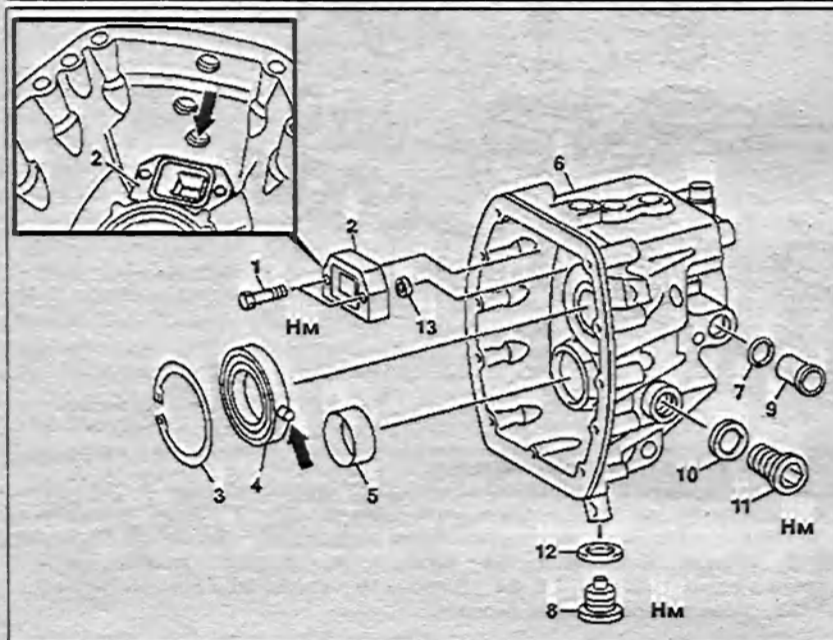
б. Задняя часть корпуса коробки передач 711.612/613:
